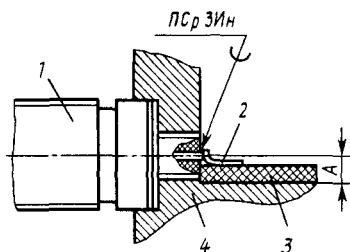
Монтаж коаксиально-полоскового соединителя (полосковый проводник и экран условно не показаны): 1—соединитель; 2—перемычка; 3—плата; 4—корпус модуля
